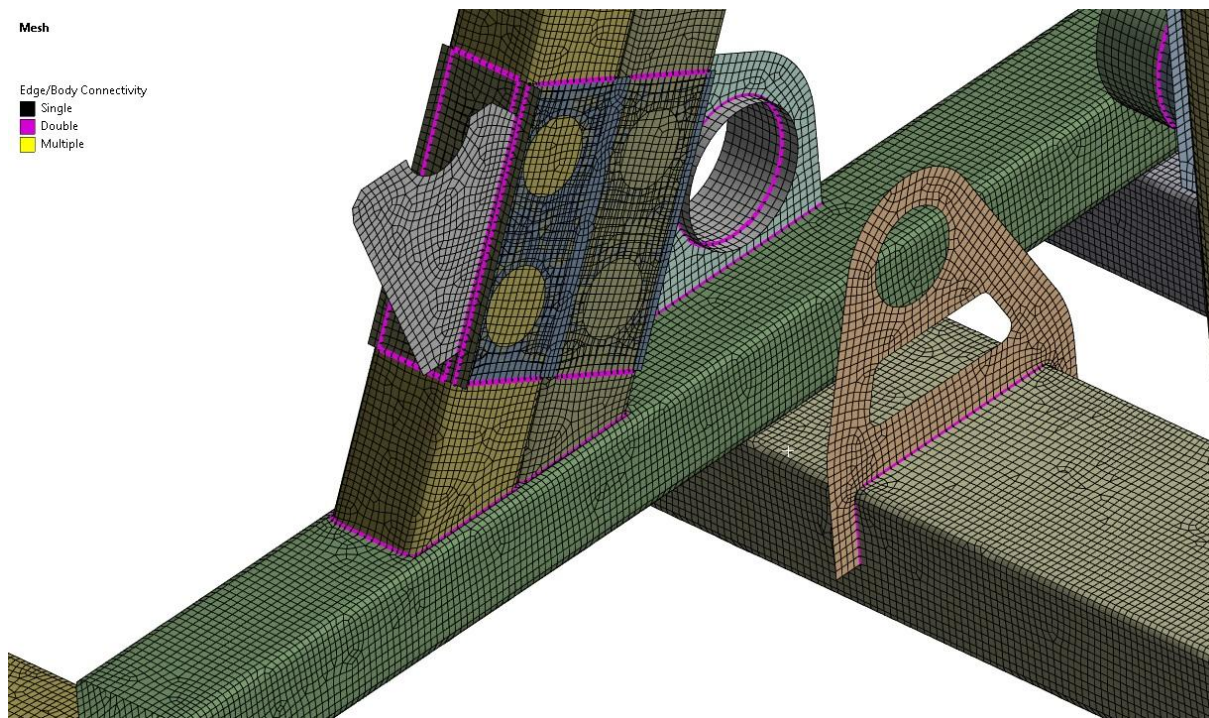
Detail držáku uchycení přímočarého pneumatického motoru brzdy nosného lana
